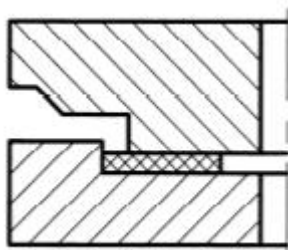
Уплотнительная поверхность типа "выступ-впадина" [72]
